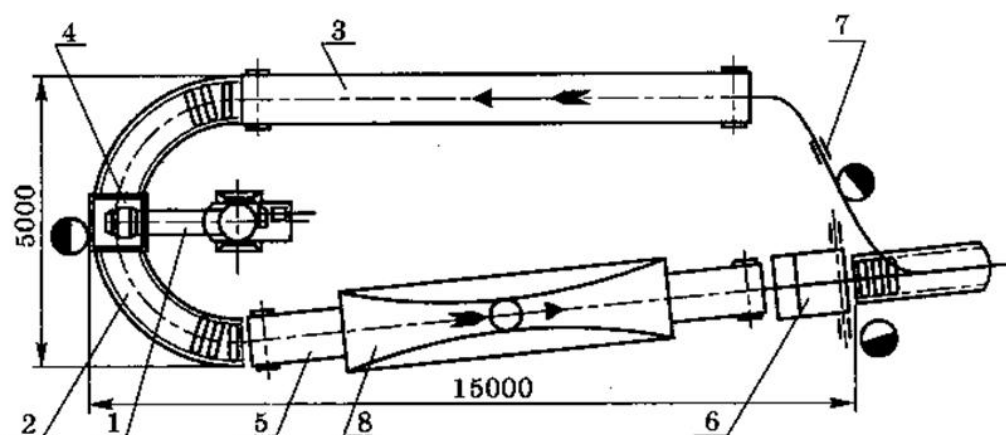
Схема механизированной линии для изготовления стержней из ХТС
